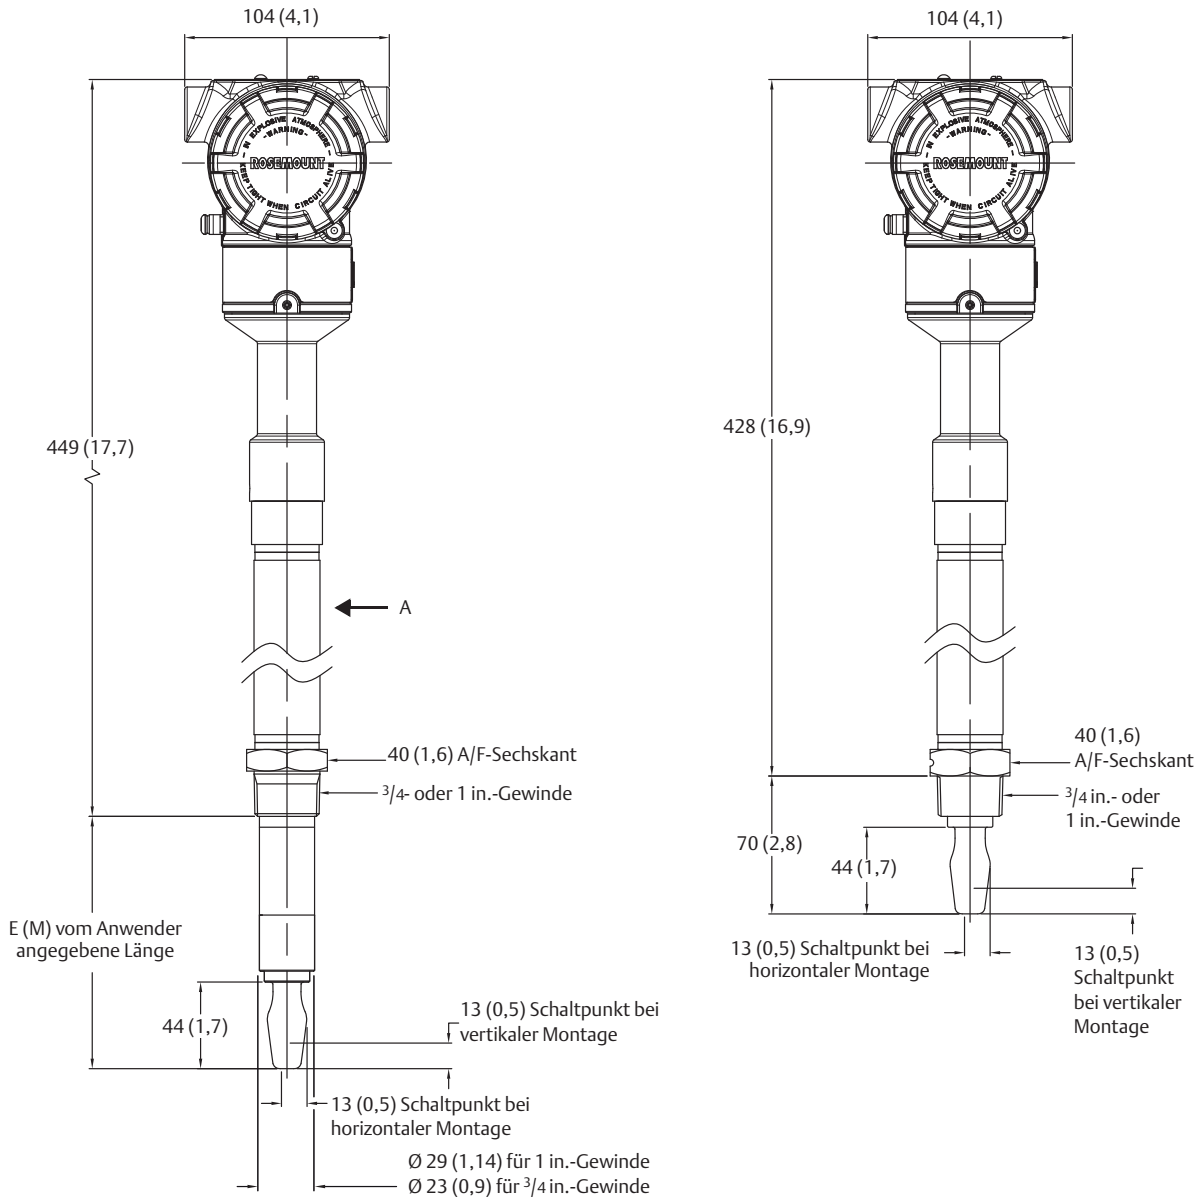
$\frac{3}{4}$ in.- und 1 in.-Prozessanschluss mit Gewinde (mittlerer Temperaturbereich, Gabel in erweiterter Länge)
